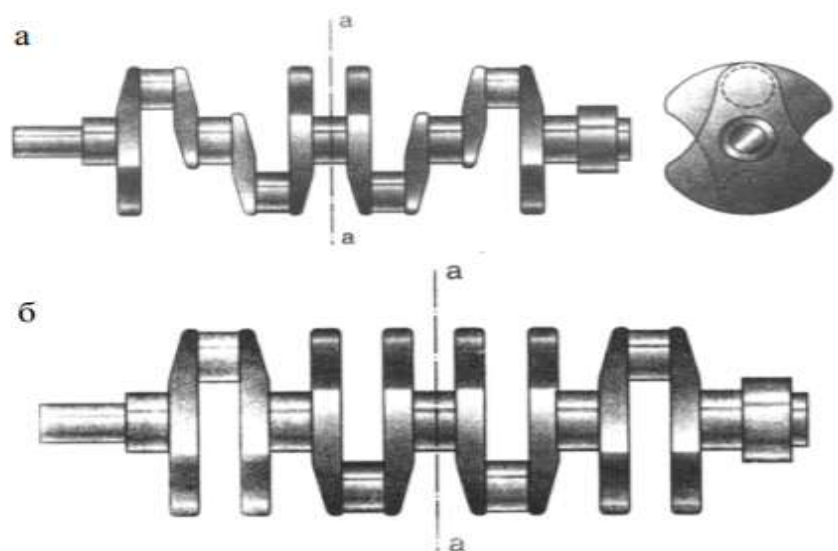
Колінчастий вал рядного чотирициліндрового двигуна:
